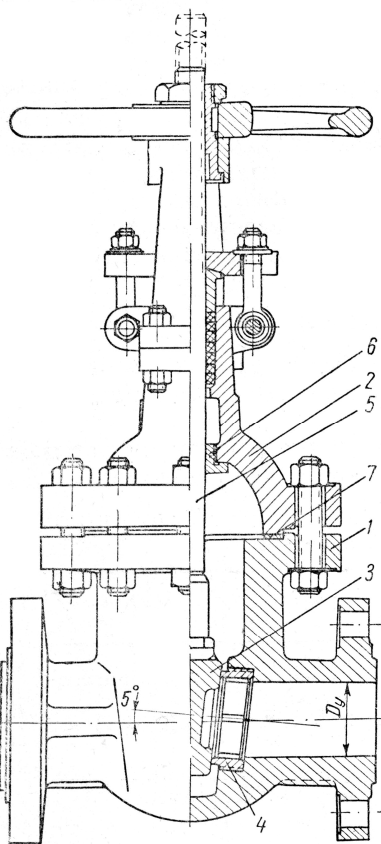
Задвижка клиновья: 1 – корпус; 2 – крышка; 3 – клин; 4 – кольцо; 5 – шпindelь; 6 – втулка сальника; 7 – прокладка
